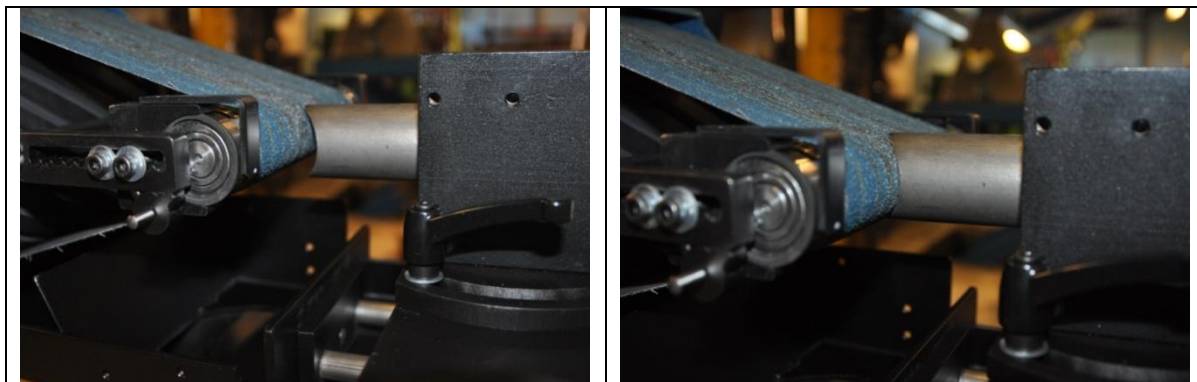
Вид держателя трубы снизу - корпус не виден.
